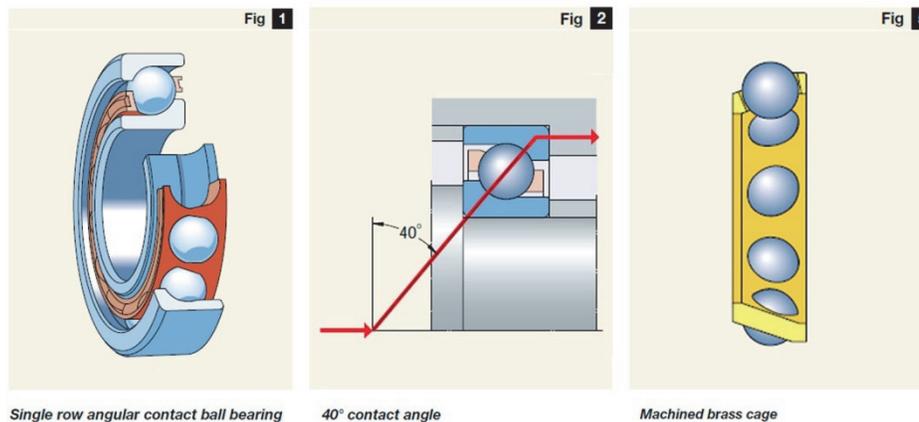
Detalles técnicos del rodamiento direccional de contacto angular. Fuente SKF
